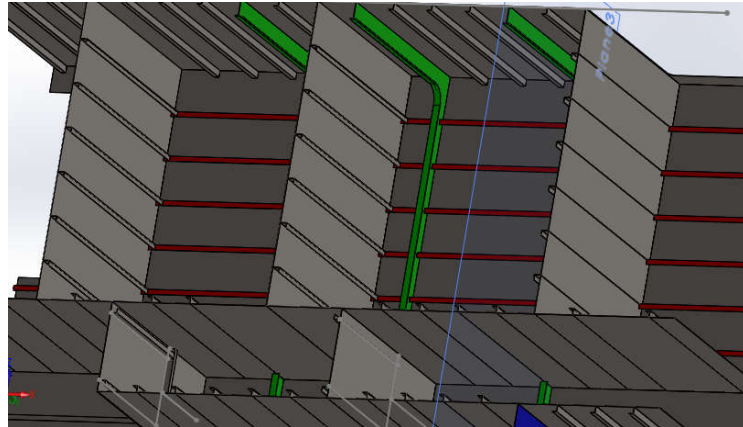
Tahap Pemodelan Konstruksi Wall
